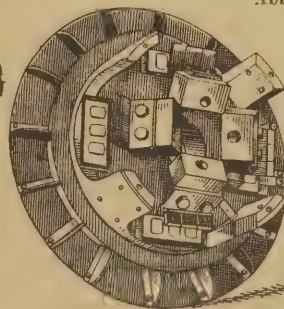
Fliehkraftschalter eines Weißberg-Simplex-Motors, geöffnet.
